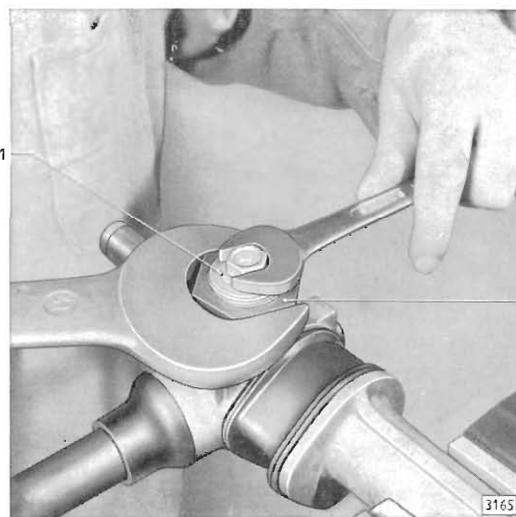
Sechskant-Gegenmutter für Einstellschraube lösen
